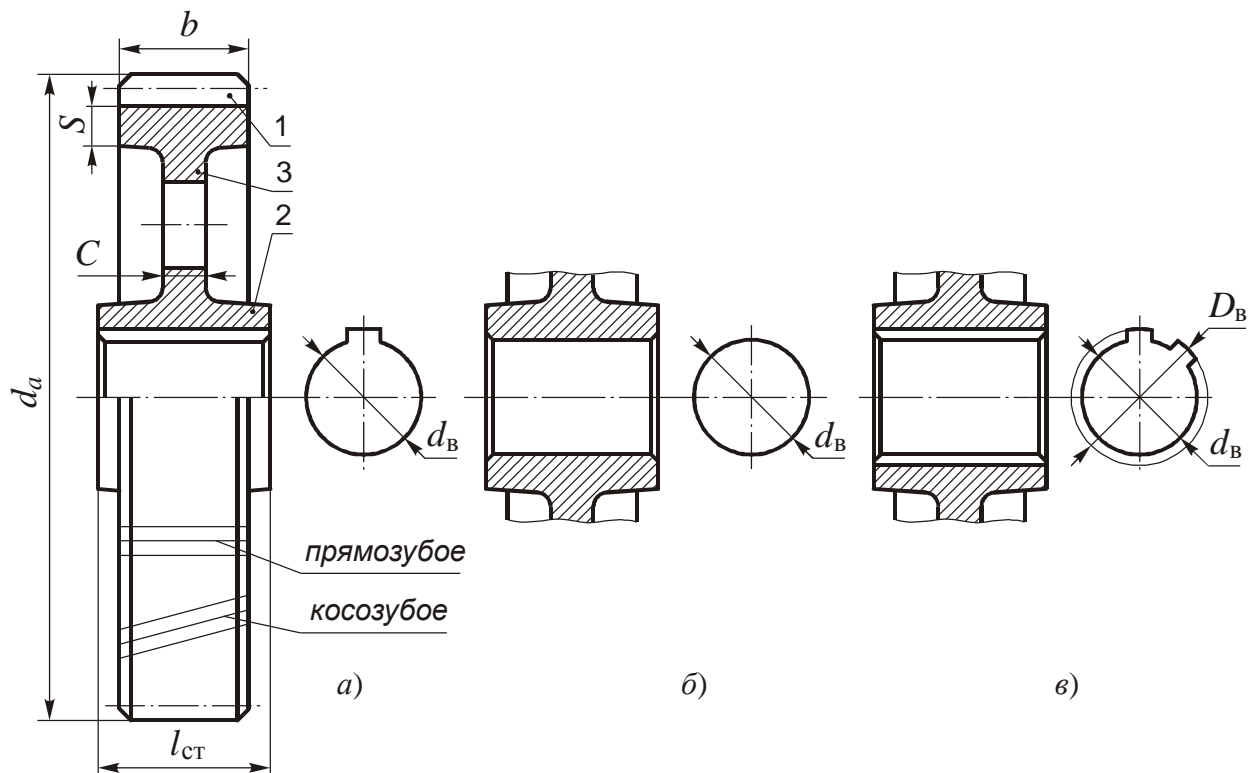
Зубчатое колесо и виды посадочных отверстий под вал:
